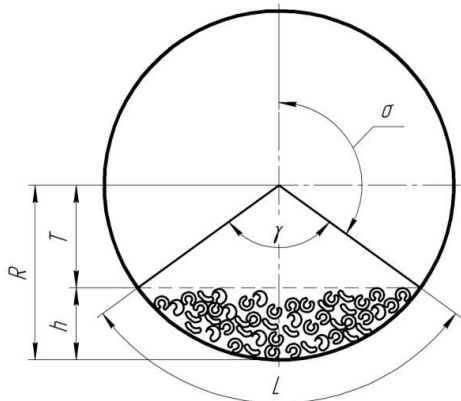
Фронтальний розтин жолоба шнекового конвєсера
